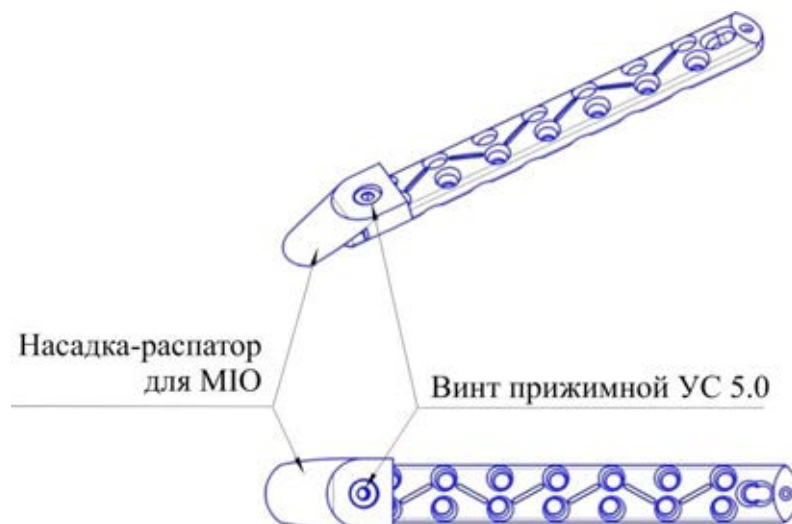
Насадка-распатор для установки двухрядной пластины с угловой стабильностью винтов
